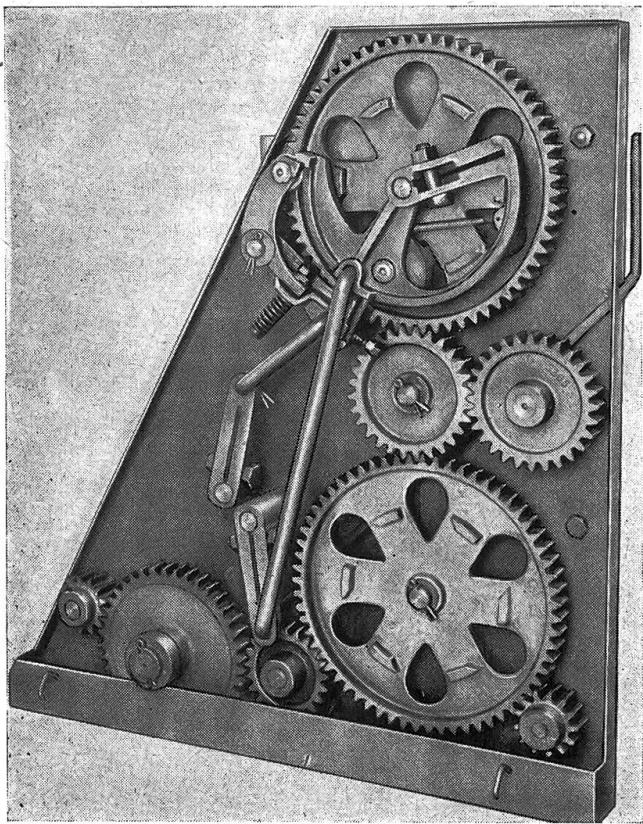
Chaque machine peut être adaptée ultérieurement en vue d'être actionnée par la prise de mouvement.
